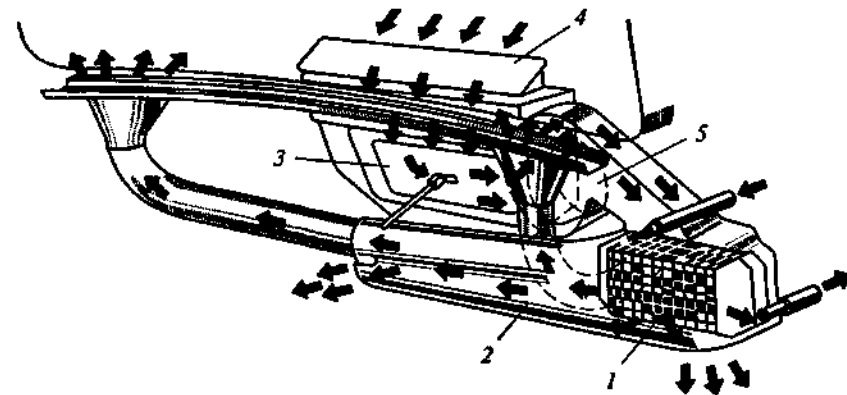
Система вентиляции и отопления кабины грузового автомобиля ГАЗ:
